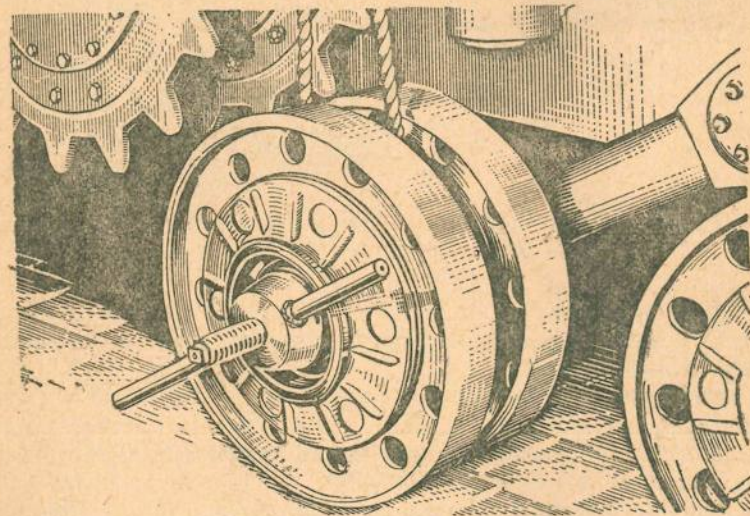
Запрессовка нижнего катка на ось балансира при помощи приспособления
